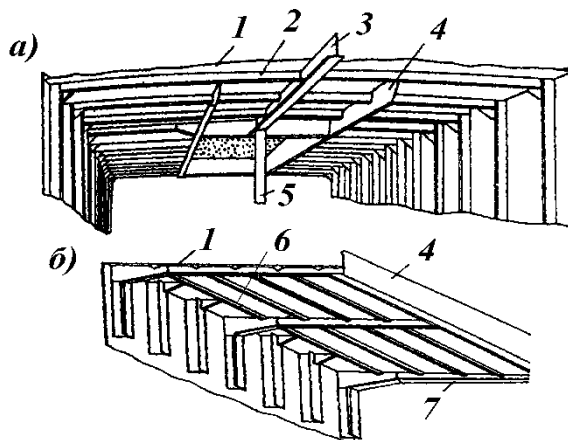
Конструкция палубных перекрытий: а – поперечная система набора, б – продольная система набора; 1 – палуба, 2 – бимс, 3 – карлингс, 4 – комингс, 5 – пиллерс
